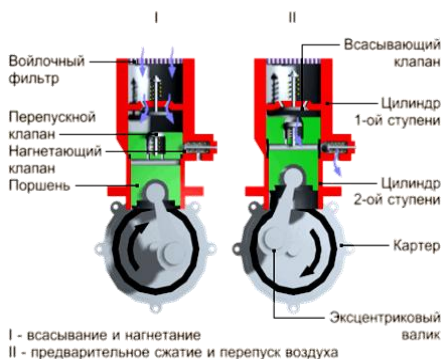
Схема работы компрессора АК-50ТЗ
